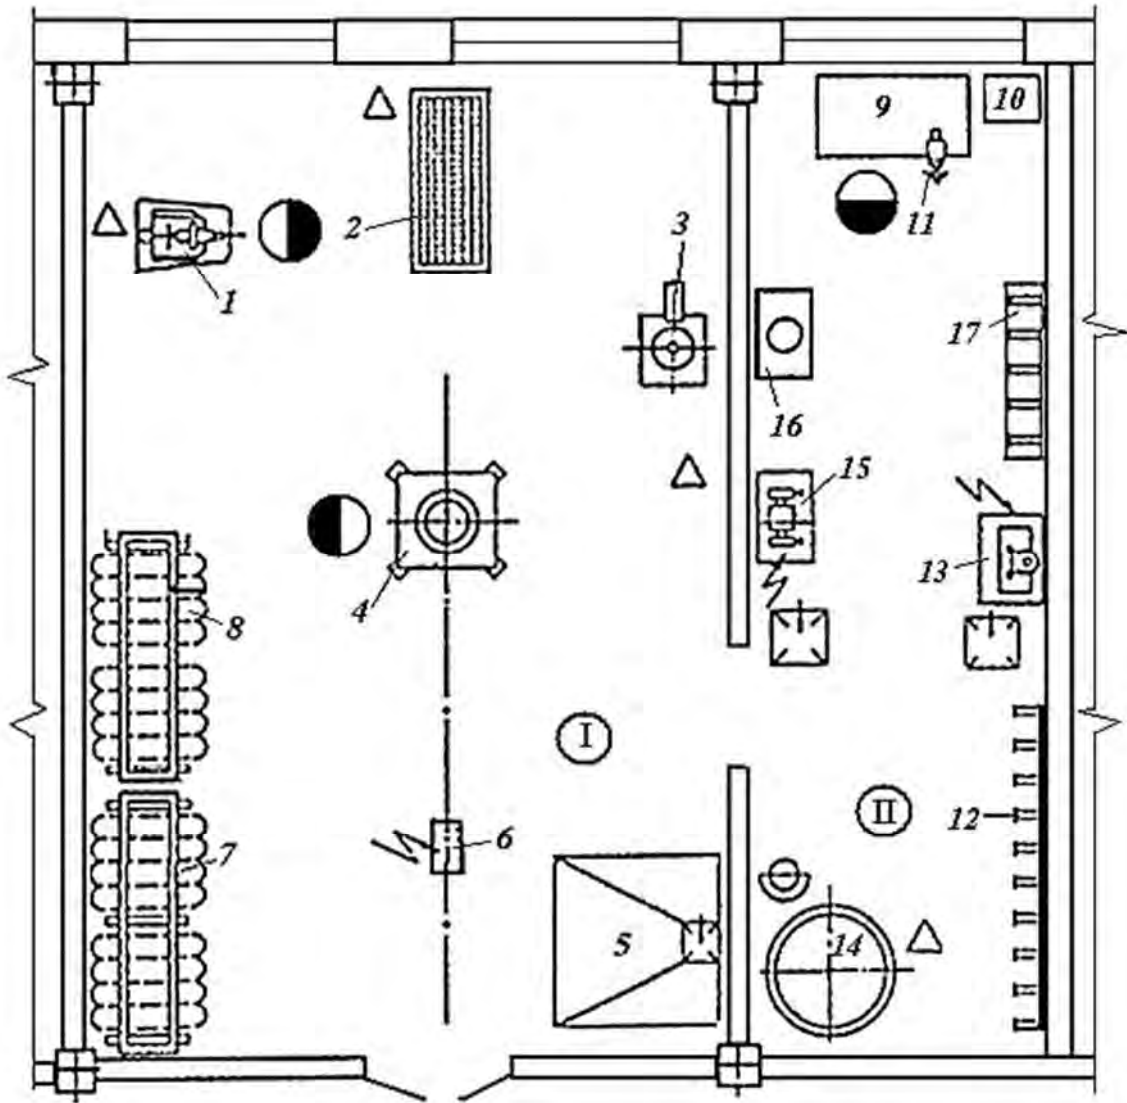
Шинный участок: I – шиномонтажное отделение; II – вулканизационное отделение; 1 – балансирующий станок; 2 – клеть для накачки шин; 3 – стенд для правки дисков колес; 4 – стенд для демонтажа шин; 5 – камера для окраски дисков колес; 6 – тельфер; 7 – стеллаж для покрышек; 8 – стеллаж для колес; 9 – верстак; 10 – ларь для отходов; 11 – слесарные тиски; 12 – настенные вешалки для камер; 13 – электровулканизационный аппарат для ремонта камер; 14 – ванна для проверки камер; 15 – шероховальный станок; 16 – ручная клеешалка; 17 – пневматический спредер
